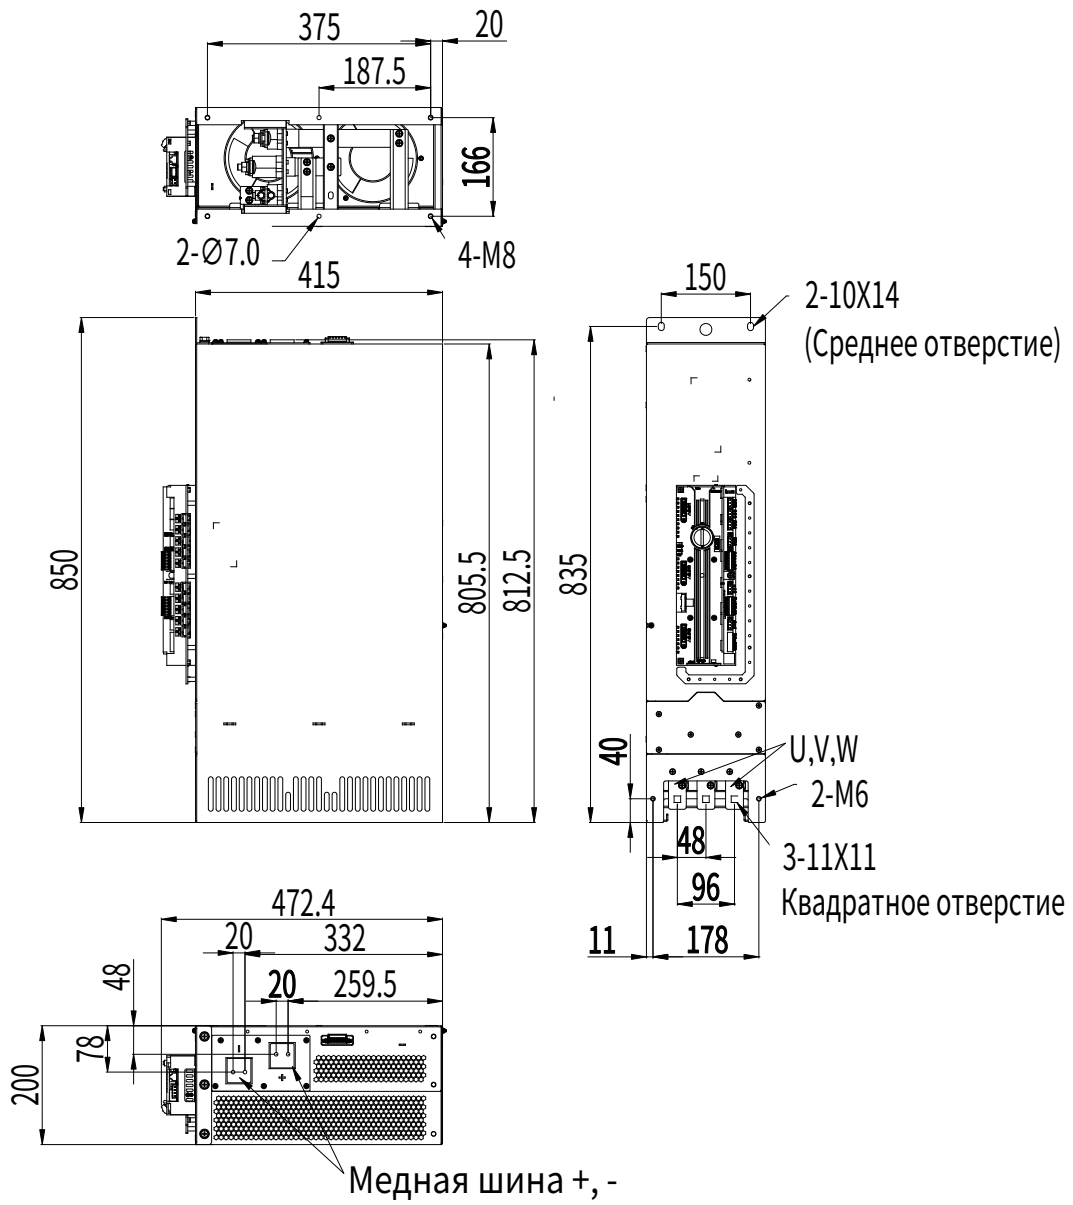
Установочные размеры инверторного блока А7i (единица измерения: мм)
